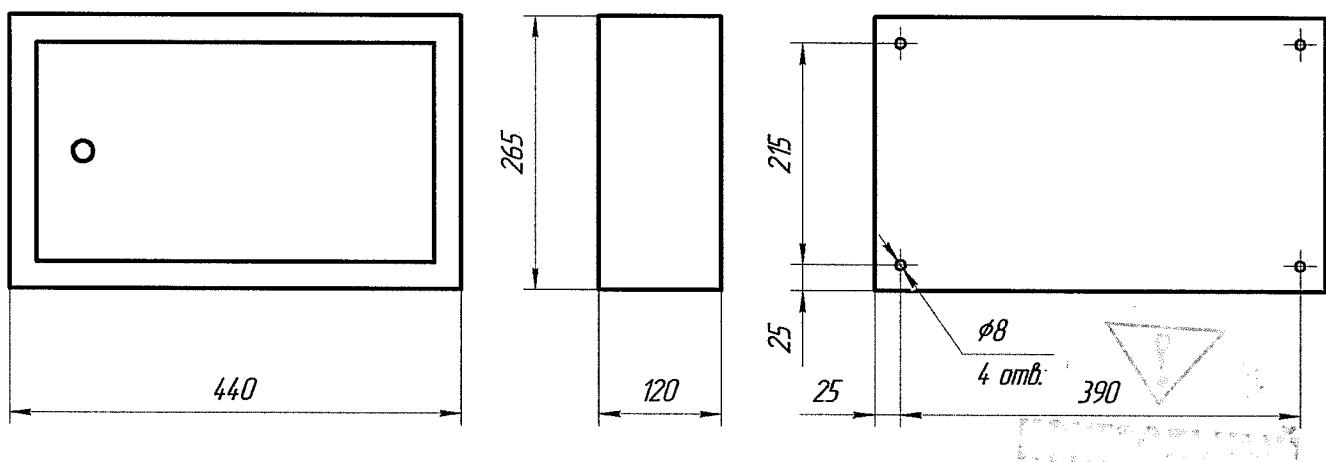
Габаритные, установочные размеры Блока интерфейсного
